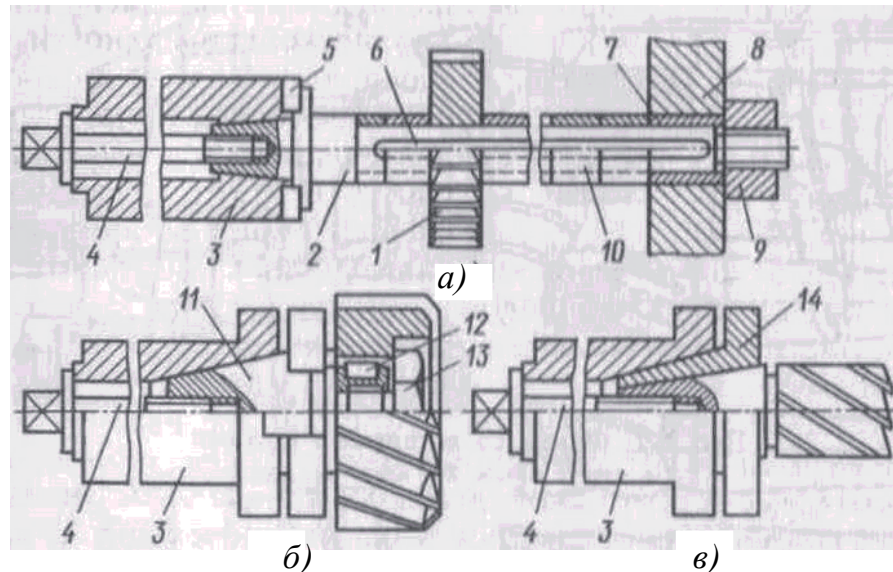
Схемы закрепления фрез: а – дисковой; б – торцевой; в – концевой
